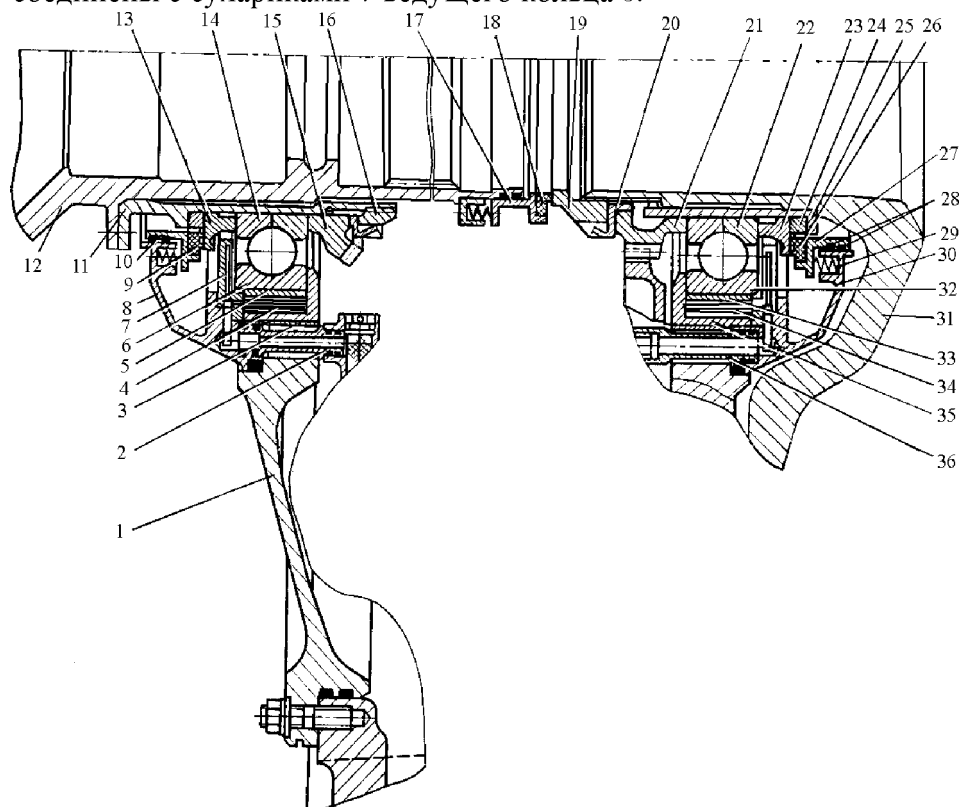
Опора роторов НД и ВД в корпусе средней опоры:
